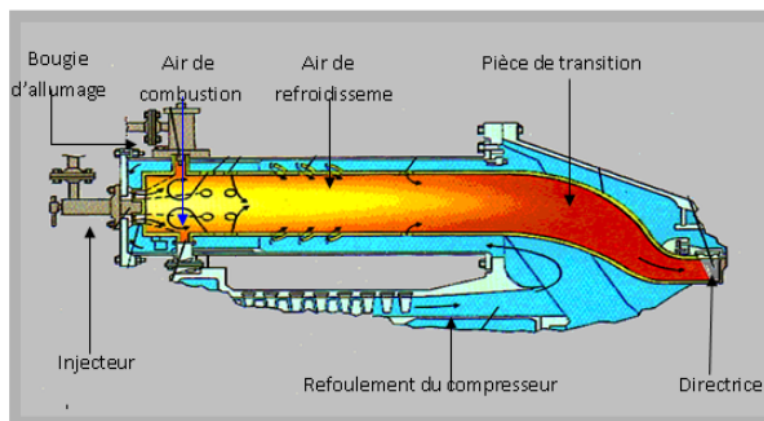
Chambre de combustion d'un turbine a gaz.
